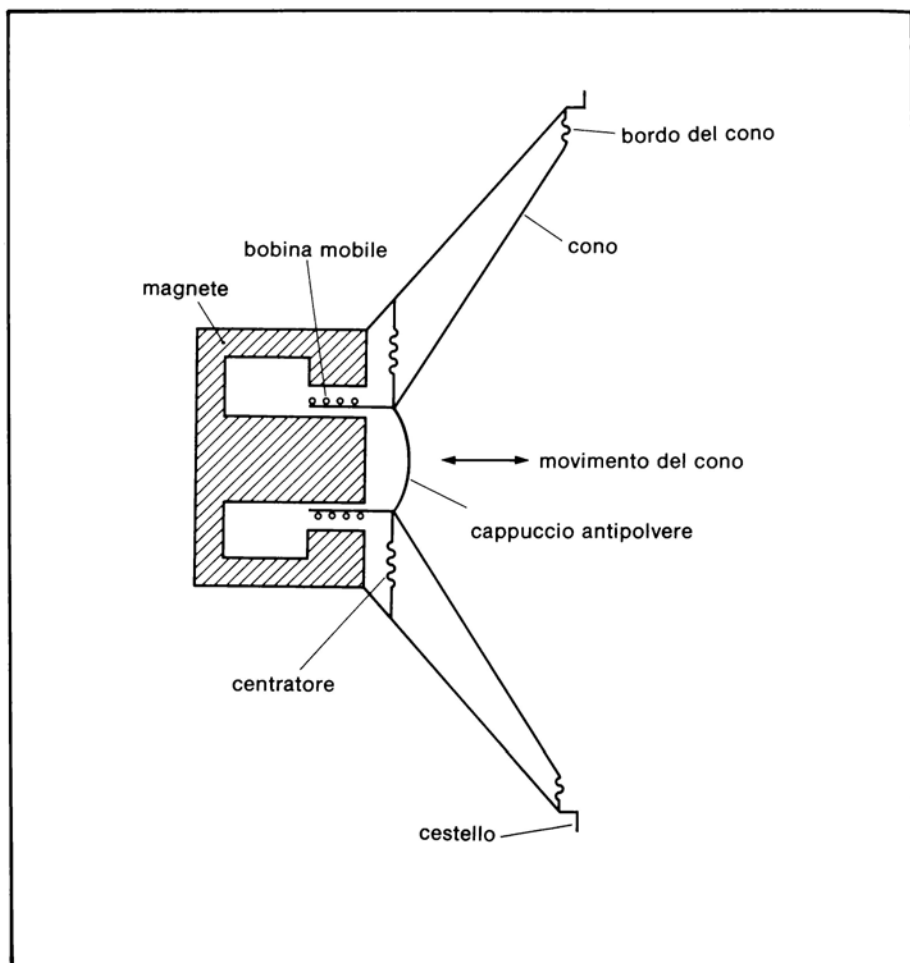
Spaccato di un tipico altoparlante a bobina mobile Magnet: = magnete; voice coil = bobina mobile; Centring device = Centratore; cone = cono; cone movement = movimento del cono; cone surround = bordo del cono; frame = cestello; dust cap = cappuccio antipolvere.
